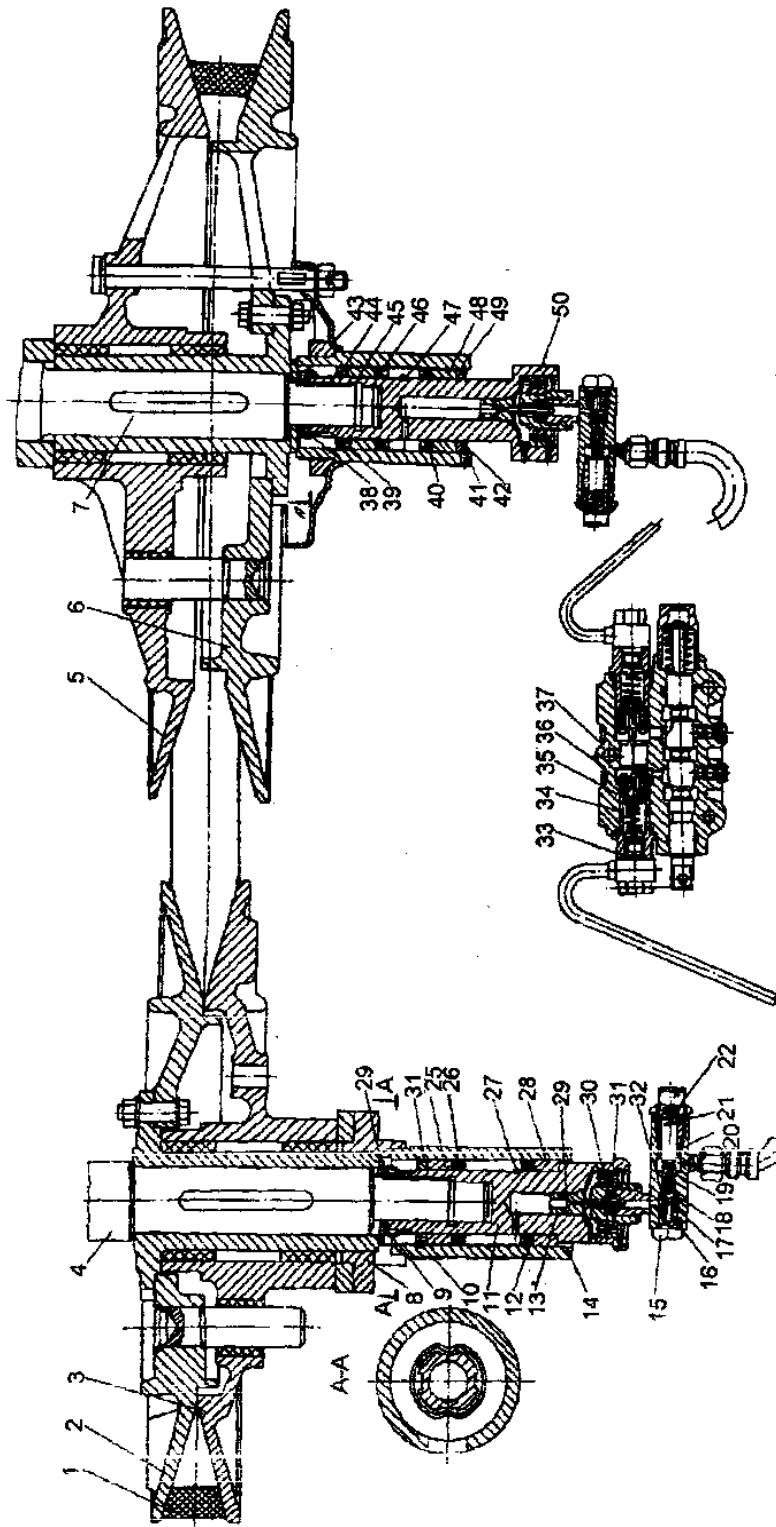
Гидрофицированный вариатор барабана: 1 – ремень; 2 – диск малый неподвижный; 3 – диск малый подвижный; 4 – вал барабана; 5 – диск большой неподвижный; 6 – диск большой неподвижный; 7 – вал главного контрпривода; 8, 13, 25, 28, 45, 48 – втулки; 9, 24, 38 – шайбы замковые; 10, 41, 44 – кольца стопорные; 11, 19, 50 – штоки; 32, 26, 31, 40, 46 – манжеты; 14, 49 – гильзы; 15 – пробка; 16, 20, 29, 30, 32, 33, 35, 36 – кольца уплотнительные; 17, 22 – пружины; 18, 23, 39, 42 – шайбы; 21 – винт; 27, 47 – кольца; 34 – клапан запорный; 37 – шток; 43 – тарелка; 51 – поршень; 52 – болт
